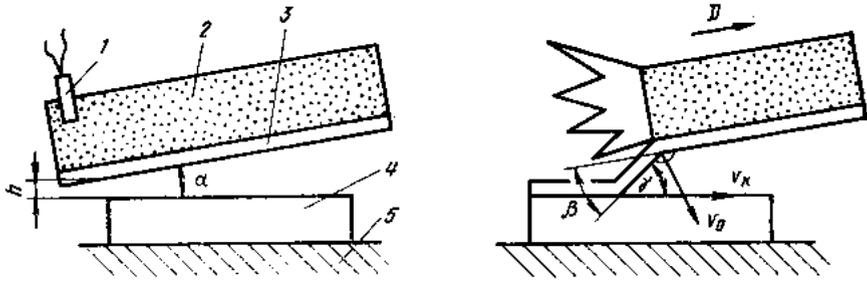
Схема сварки взрывом под углом:
